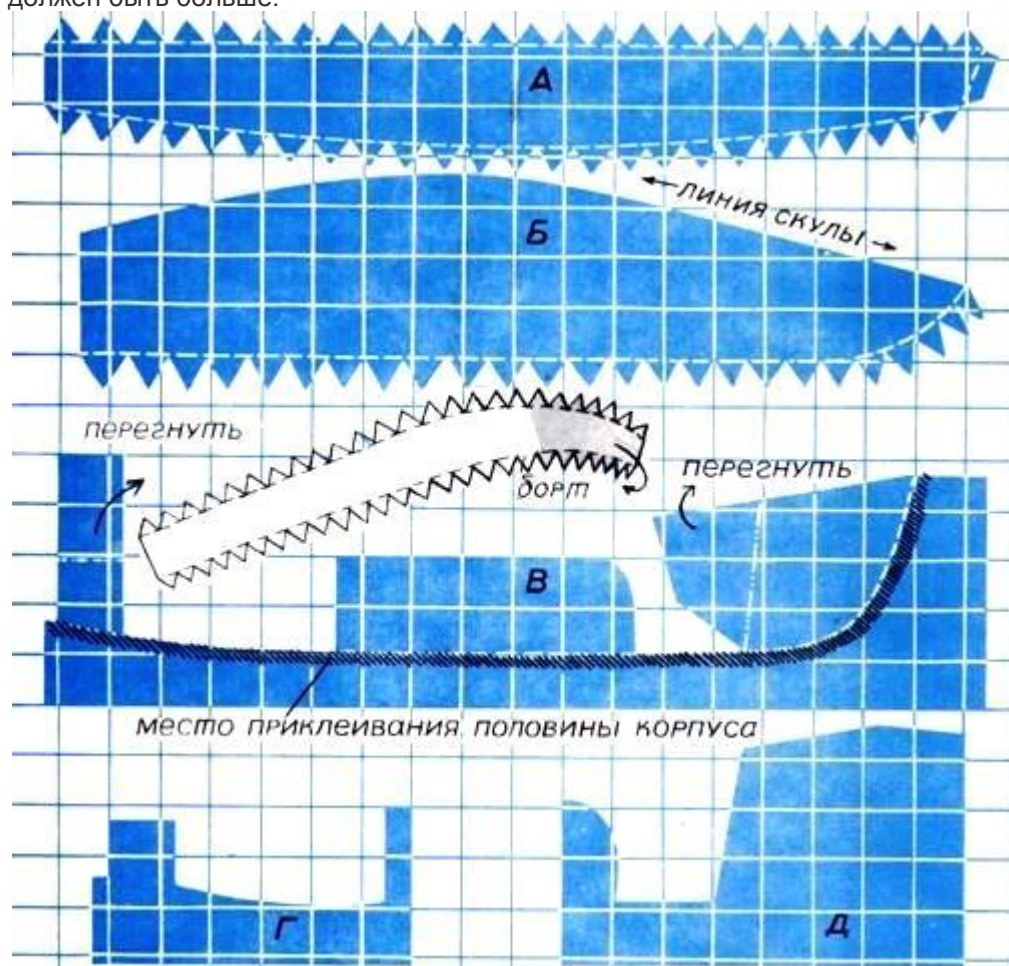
Развертка корабля типа "швертбот" с выдвижным килем.
